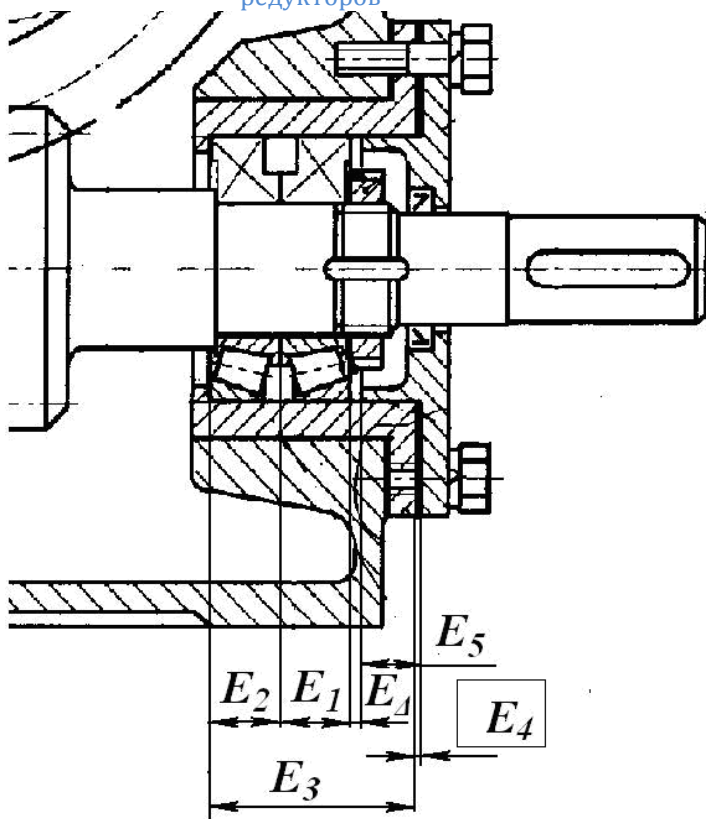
Схема размерной цепи  $E$  в случае двойной подшипниковой опоры
